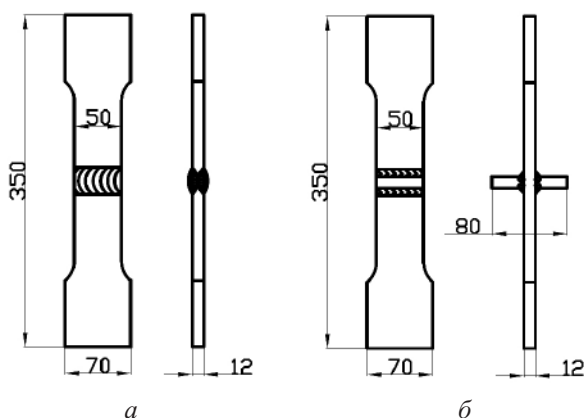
Форма и геометрические размеры образцов стыковых (а) и тавровых (б) сварных соединений.
